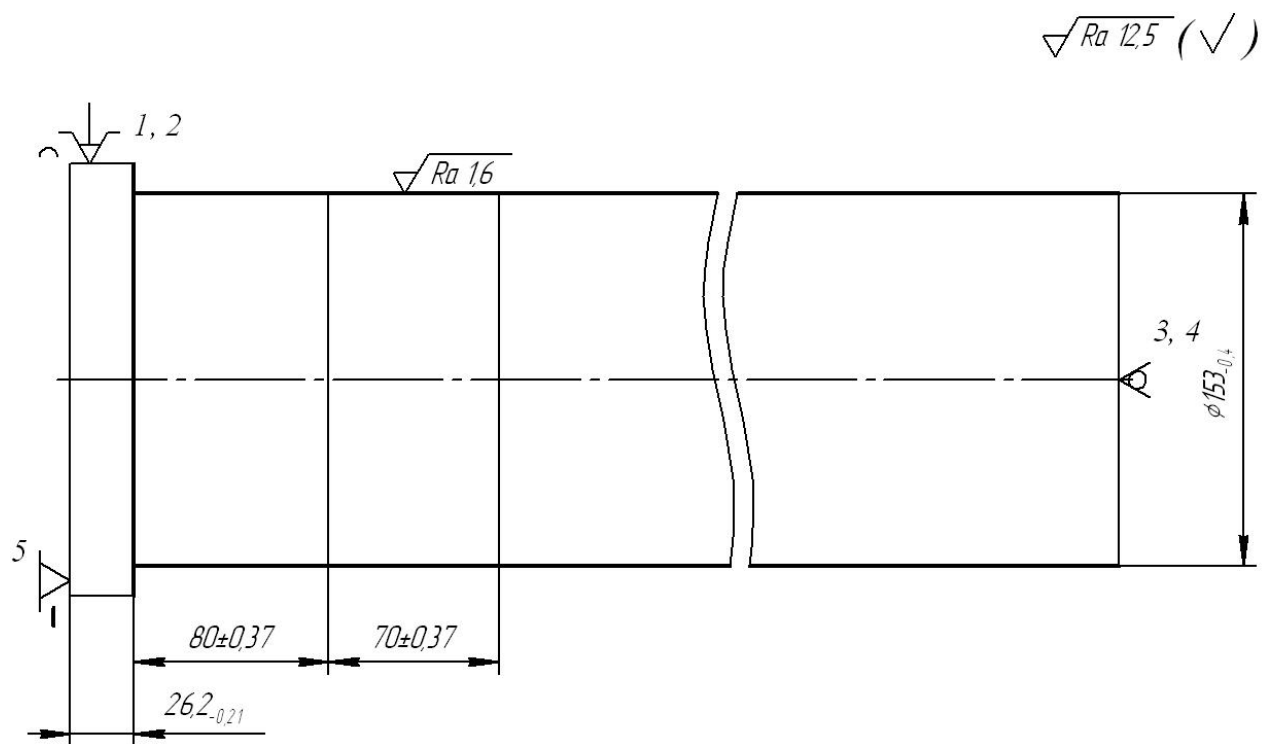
Альтернативна схема базування заготовки на операції токарно-гвинторізній 020, установ А
